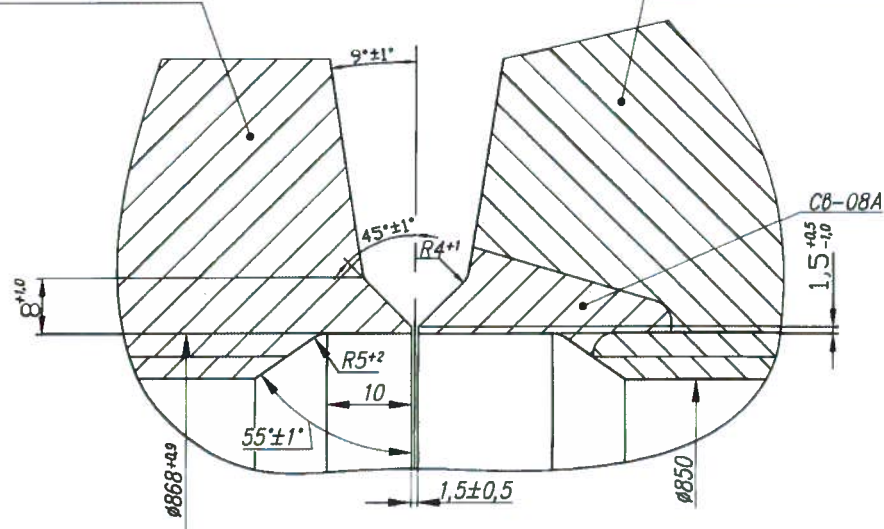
Разделка кромок монтажного соединения ГЦТ с патрубками корпуса реактора
